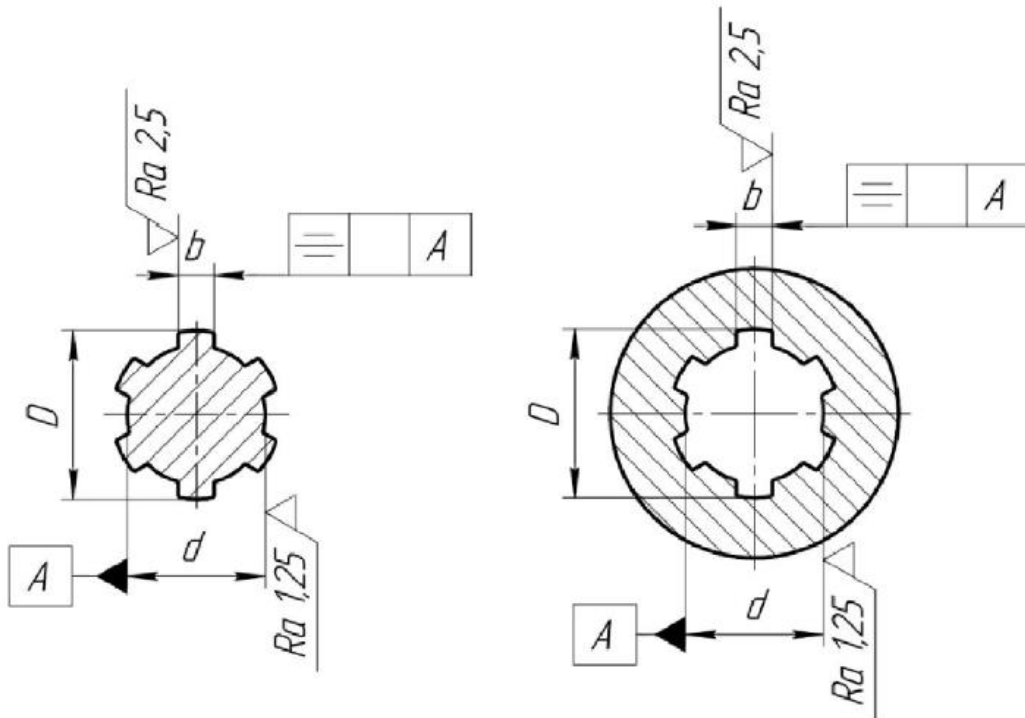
Базові поверхні, чистота обробки та допуски форм і розташування поверхонь шліцьового прямобічного з'єднання при центруванні за внутрішнім діаметром
